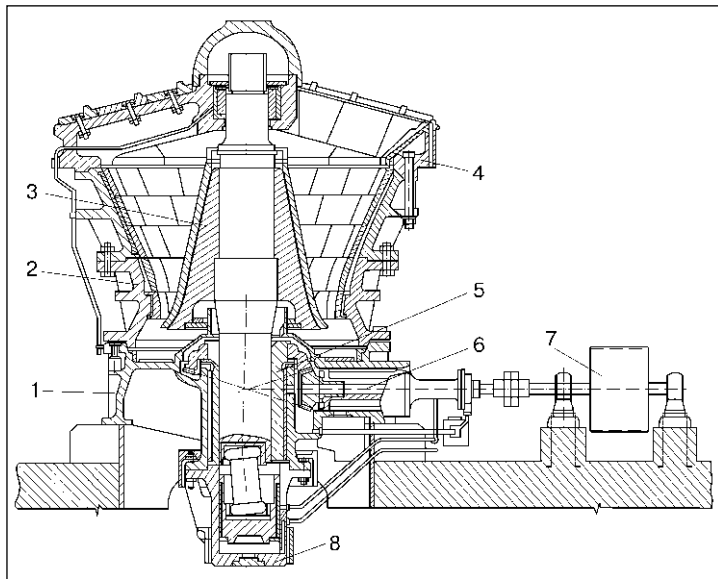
Конусная дробилка ККД 1500/180: 1 — нижняя часть станины; 2 — чаша; 3 — дробящий конус; 4 — траверса; 5 — эксцентрик; 6 — приводной вал; 7 — привод; 8 — крышка
